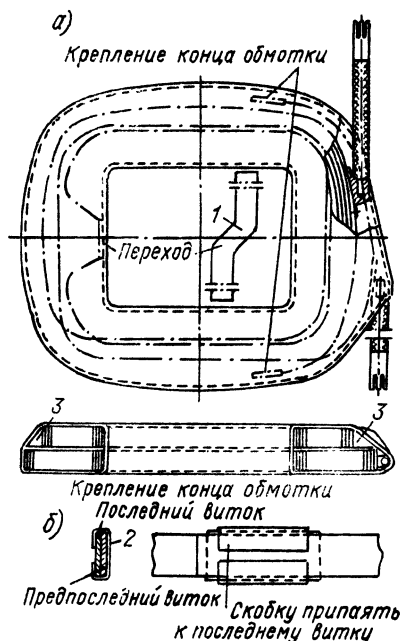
Катушка главного полюса из полосовой меди с кабельными выводами: а — катушка; б — крепление последнего витка
